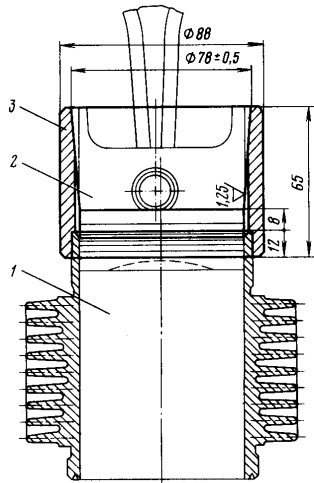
Оправка для установки поршня с кольцами в цилиндр:
